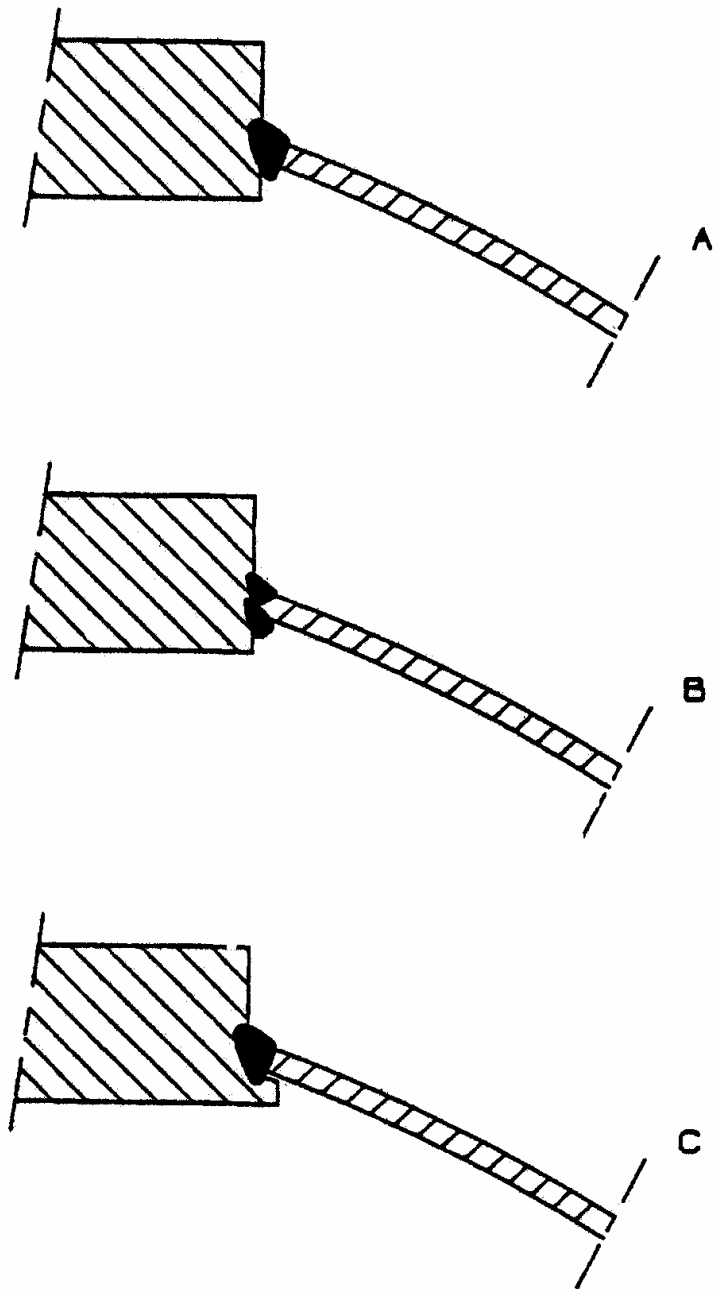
Beispiele für geschweißte Bolzenplatten
